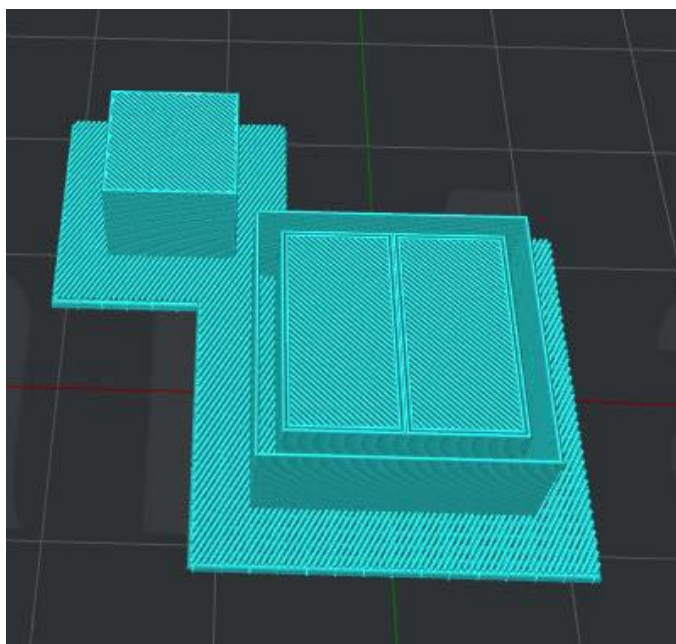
Nastavení Wipe Wall na "Vertical".
